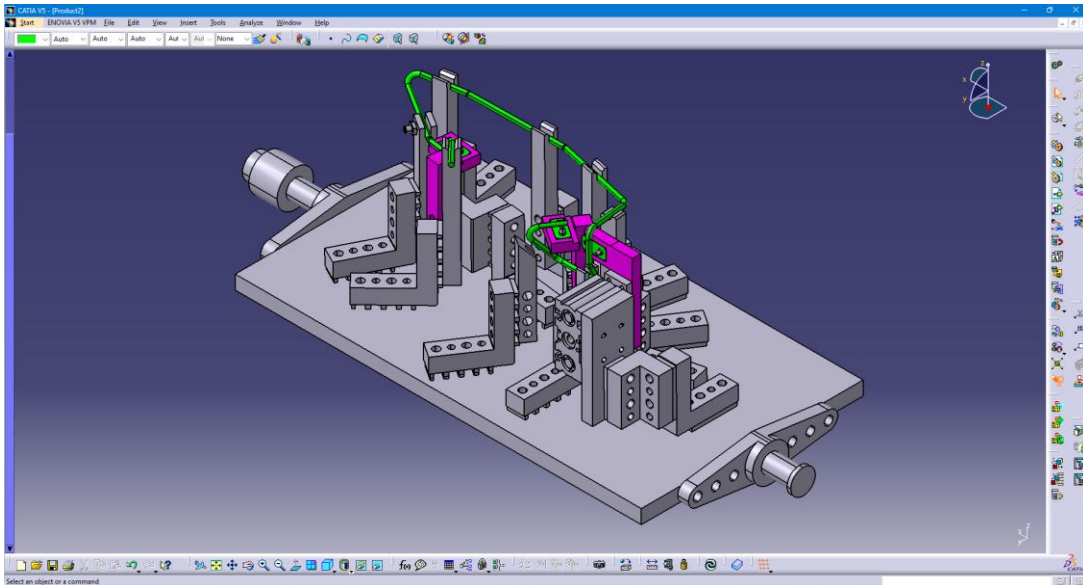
DISEÑO ORIGINAL DE WELDING [27]
